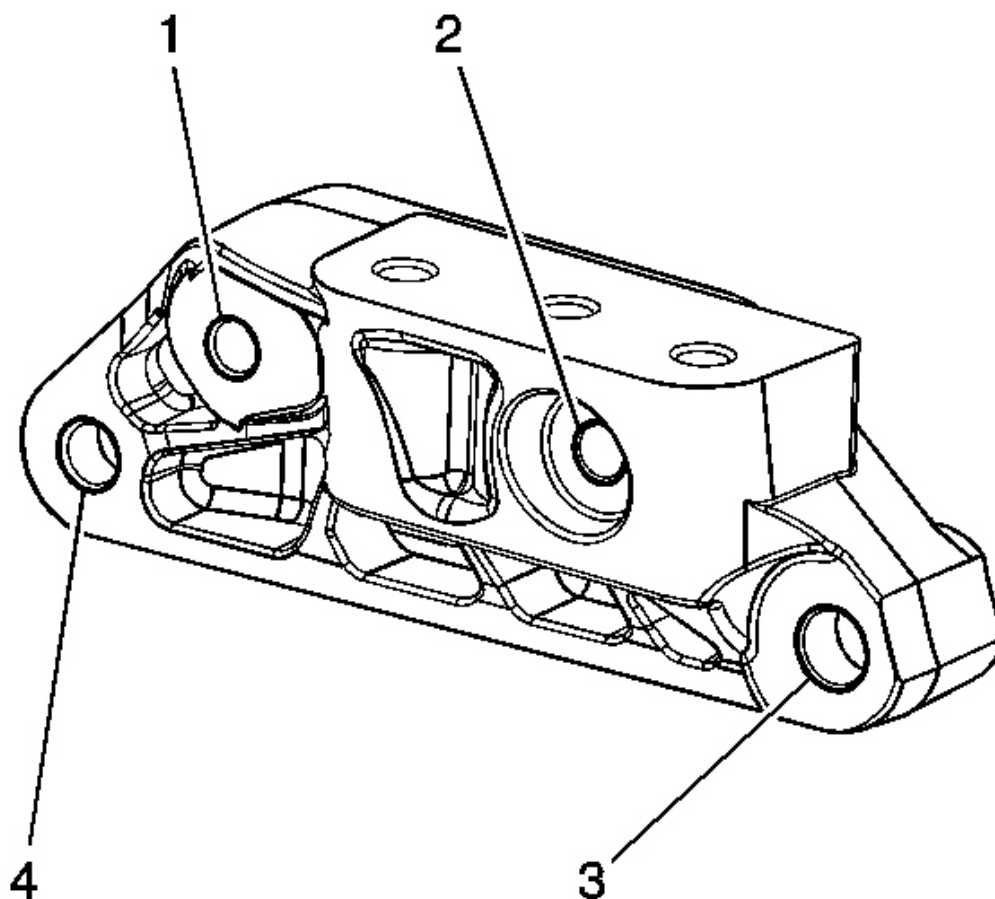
Vista del lado derecho del motor Soporte de montaje
